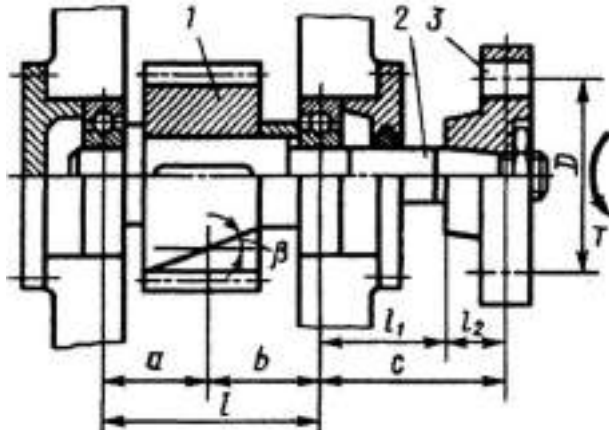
Вал с элементами, расположенными на нем: 1 – шестерня; 2 – вал; 3 – полумуфта
